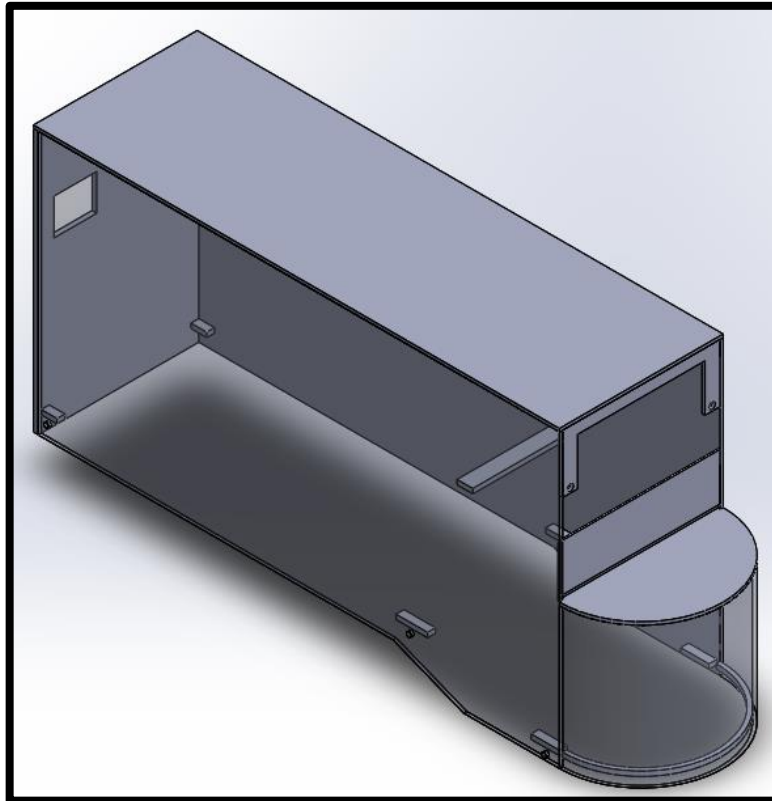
Carcasa exterior una vez soldados los componentes. Fuente: Propia.
